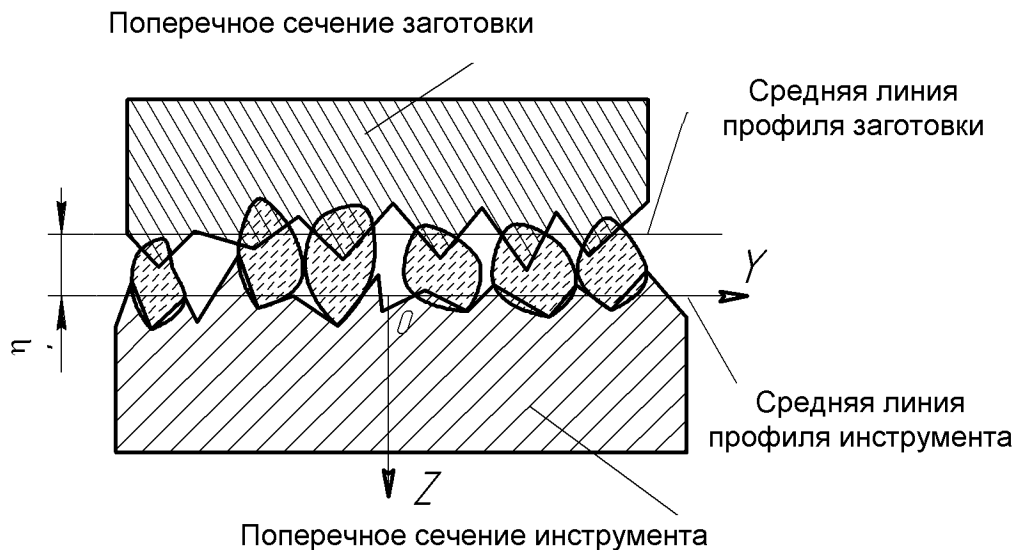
Схема контакта поверхности заготовки с поверхностью доводочного инструмента
